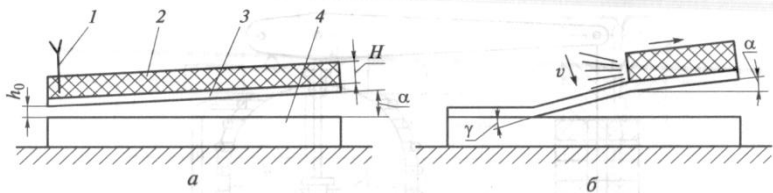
Схема сварки взрывом: а — перед взрывом; б — в момент взрыва; 1 — детонатор; 2 — взрывчатое вещество толщиной H , 3, 4 — свариваемые заготовки
